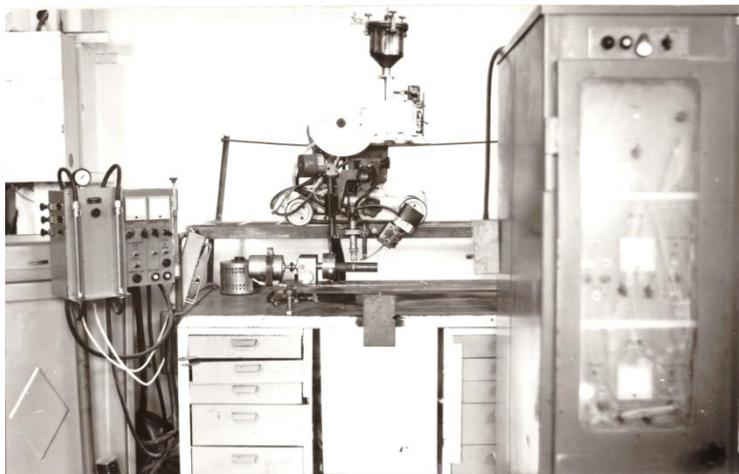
Установка для сварки поворотных стыков трубопроводов
